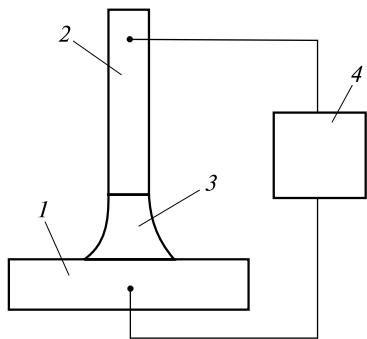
Схема электрической цепи дуговой сварки:
